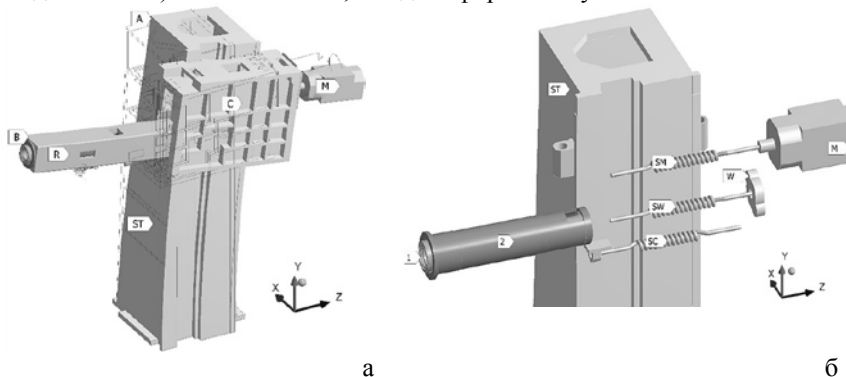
СФР-станок типа «Подвижная стойка» (а; А или ST – стойка; В – шпиндельный узел, со шпинделем 1 и гильзой 2; С – суппорт; R – ползун; М – главный двигатель) и комплект ОКС (б; пружина SM и двигатель М, пружина SW и груз W, пружина SC (осевая ШВП) и вес ползуна R)
